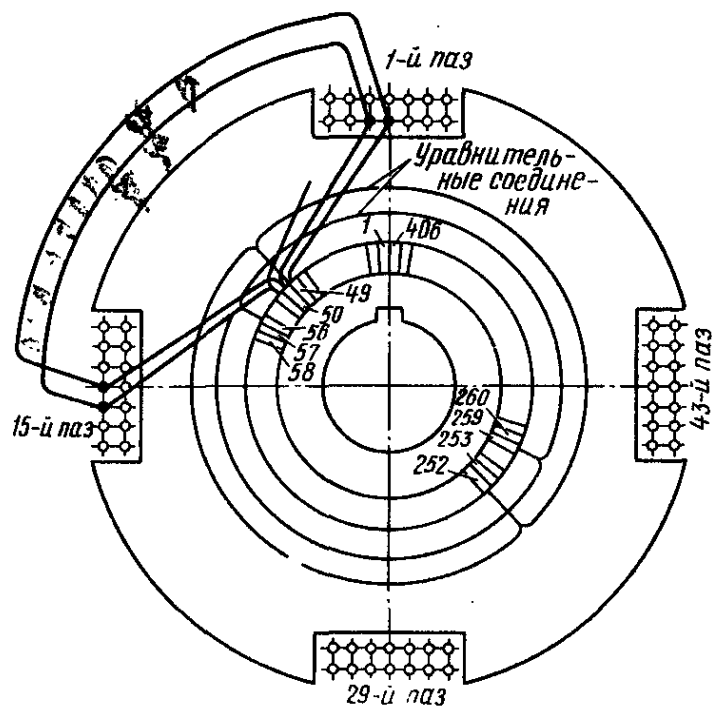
Схема соединения обмотки якоря тягового двигателя НБ-406Б с коллекторными пластинами
